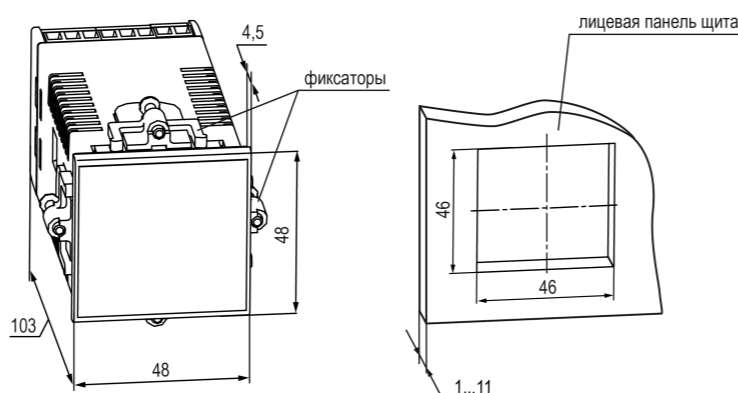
Габаритные размеры корпуса Щ5 и монтажного отверстия в щите
